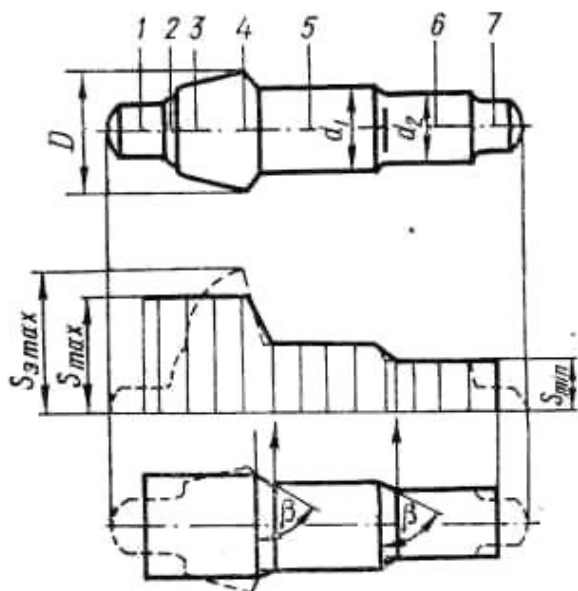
Схема побудови профілю вальцьованої заготовки
